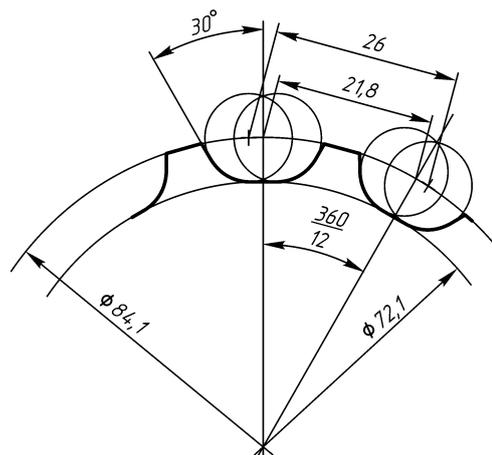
Профиль зубьев и размеры неподвижного колеса волновой зубчатой передачи с невращающейся втулочно-роликовой цепью
